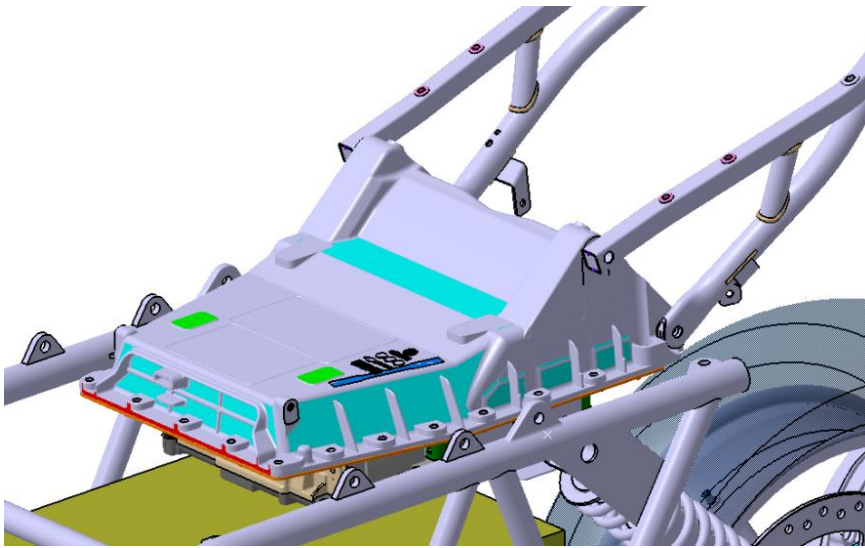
Alternative Knotenpunkte Rahmenkonstruktion
